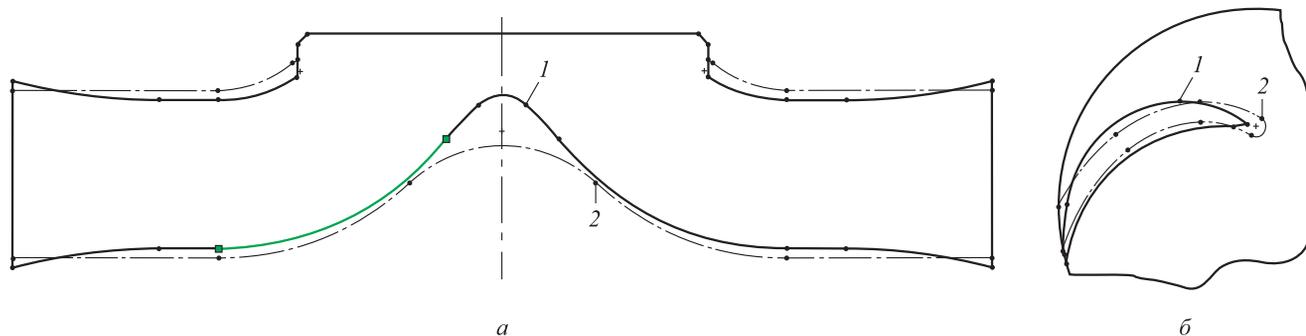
Профиль конструкции рабочего колеса (а) и лопатки (б):
